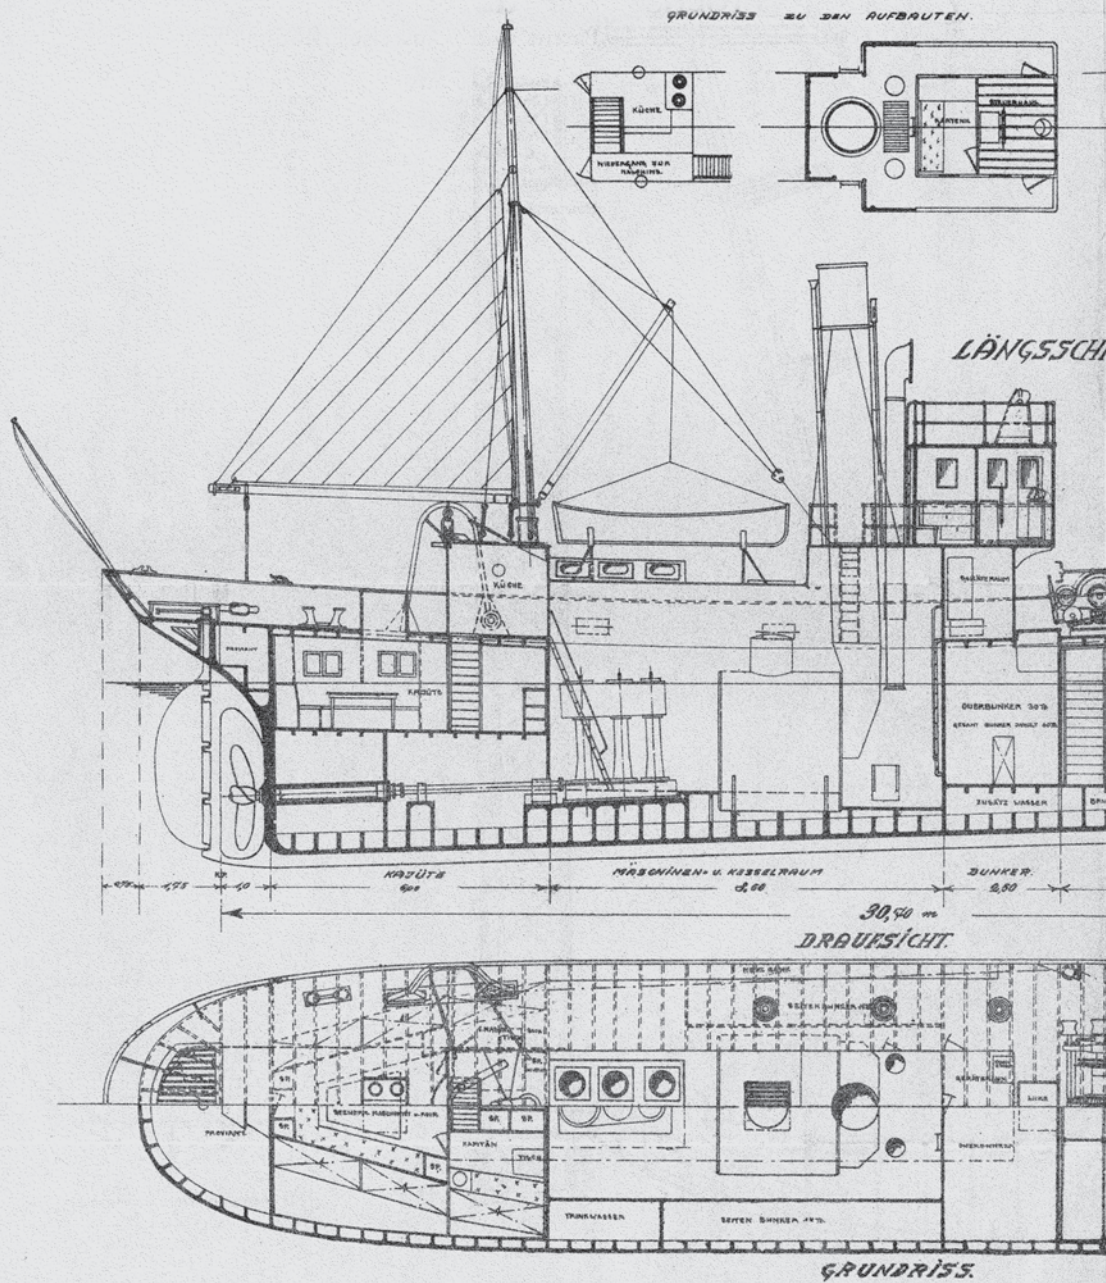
Längsschnitt und Grundriss für einen Fischdampfer aus Eisenbeton nach dem »Patent Rüdiger«.
